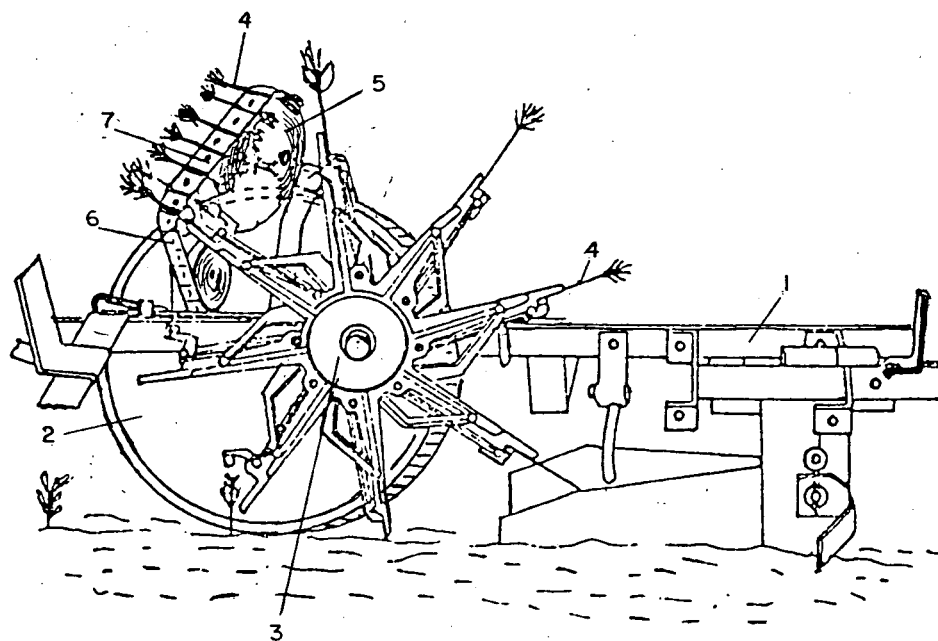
Concepção utilizando braços plantadores [7].
